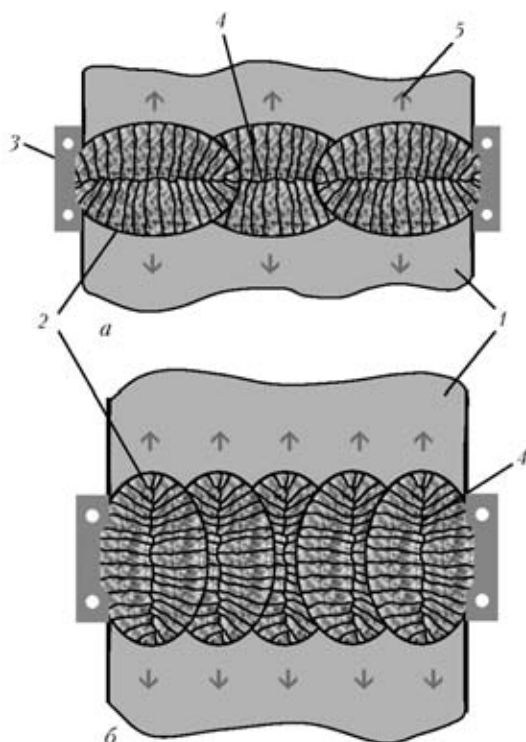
Схемы расположения зон (плоскостей) слабины в металле слоев многослойного шва при выполнении ЭШС плавящимся мундштуком с установкой плавящихся мундштуков вдоль оси разделки кромок (а) и поперек (б): 1 — свариваемая кромка; 2 — форма слоя сварного шва в поперечном сечении; 3 — формирующая накладка; 4 — зона слабины (плоскость); 5 — вектор усадочных сил
